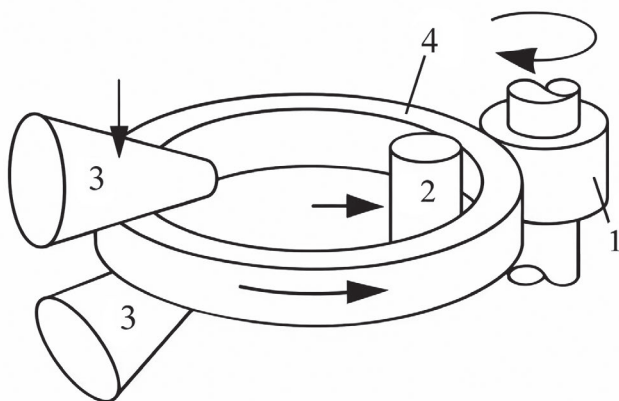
Схема кольцераскатки: 1 – главный валок; 2 – дорновой валок; 3 – осевые валки; 4 – кольцевая заготовка
